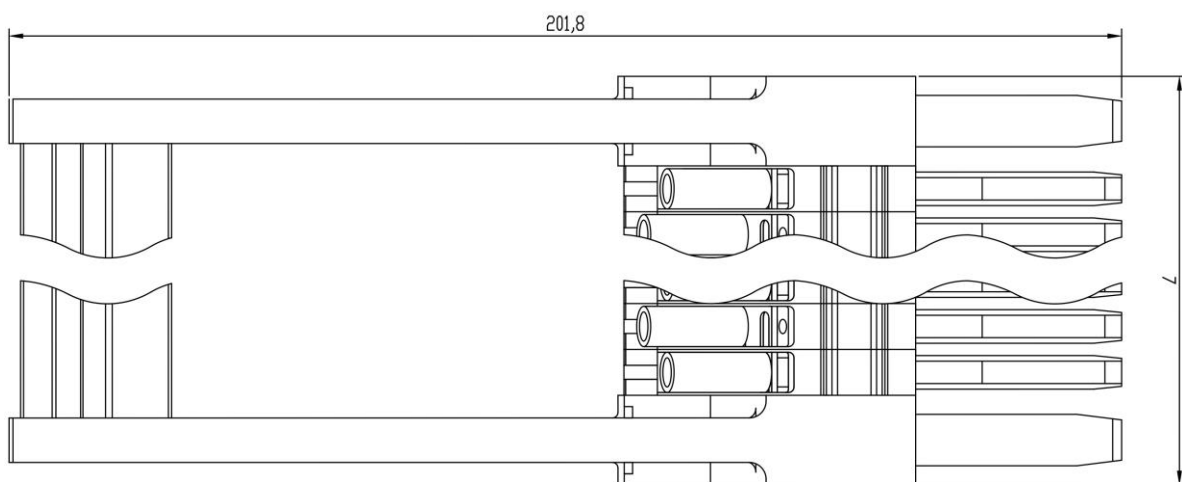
Общий вид тестовой крышки ЭПТК. Вид сверху.
